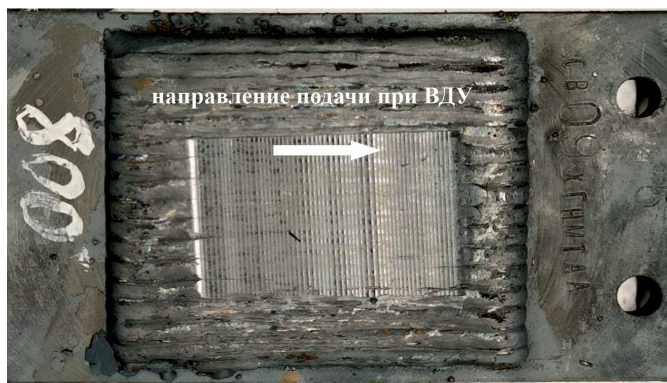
Образец из стали 09ХГМНТАА после ВДУ при 800 °С
